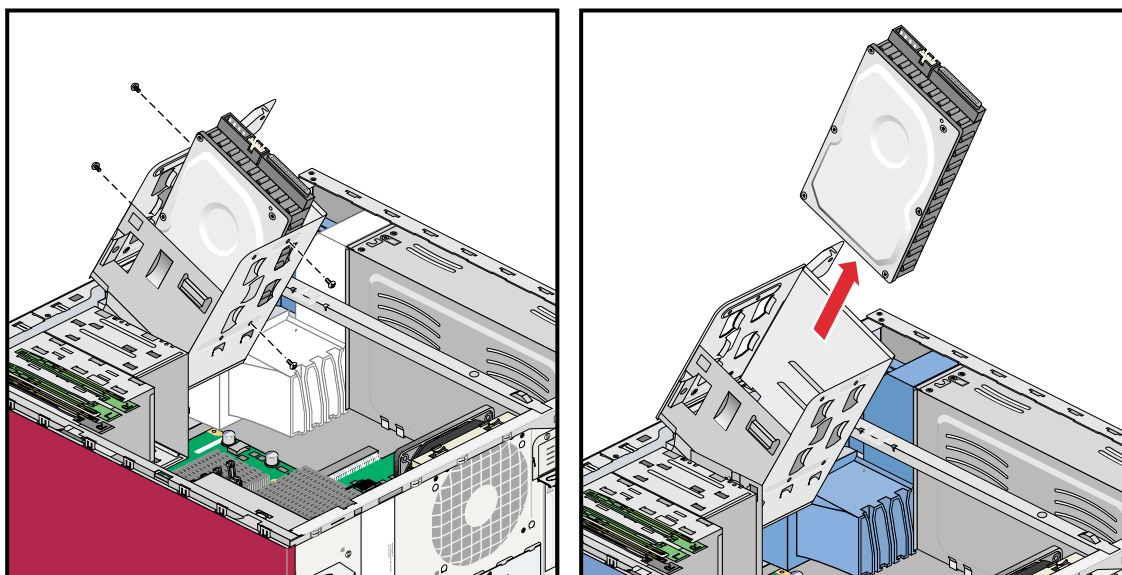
Entfernen des Festplattenlaufwerks
